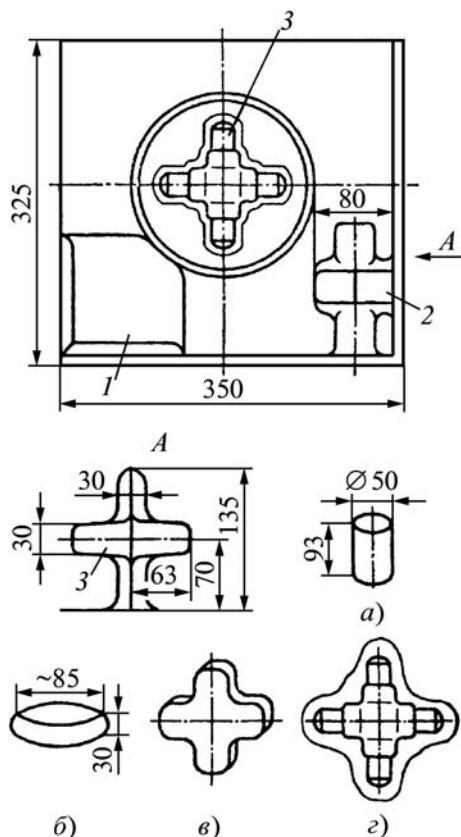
Штамп со специальным формовочным ручьем и переходы штамповки крестовины: а — исходная заготовка; б — заготовка после осадки; в — заготовка после формовочного ручья; г — отштампованная поковка с облоем; 1 — площадка для осадки; 2 — формовочный ручей; 3 — окончательный ручей
